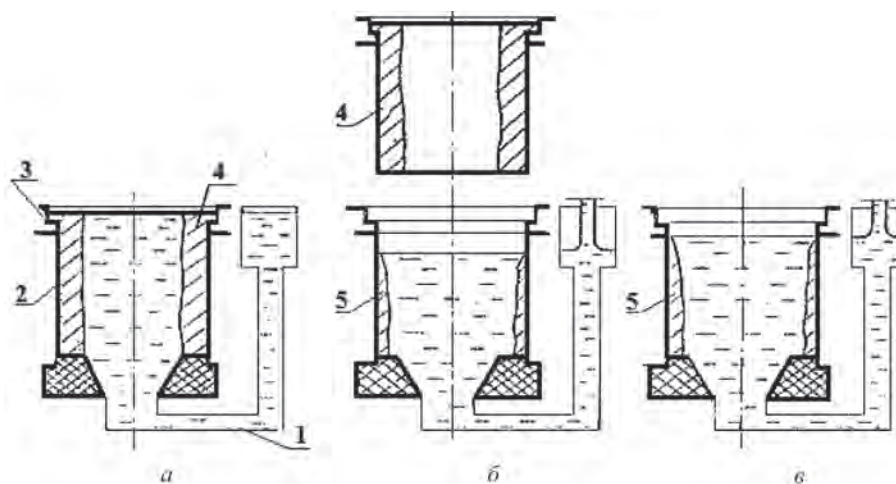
Принципиальная схема литья полых заготовок намораживанием без стержня: 1 – литниковая система; 2 – стационарный кристаллизатор; 3 – подвижный кристаллизатор; 4 – сформированная отливка; 5 – формирующаяся отливка
